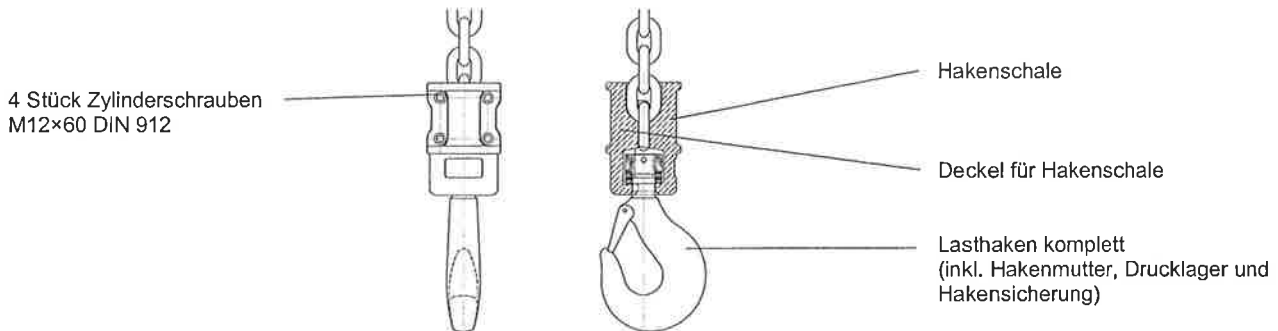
Aufbau des Hakengeschrirs für Kette 16x45 mm
